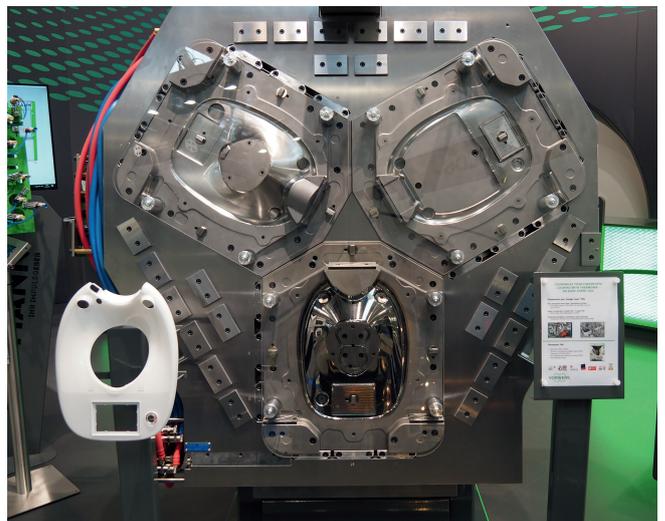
Drei Stationen, drei Komponenten: Drehtellerwerkzeug für die Bedienblende des Thermomix TM5 (© Hanser/C. Doriat)
